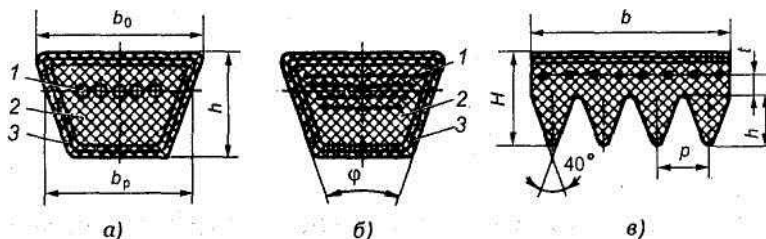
Конструкции клиновых ремней: а — кордшнуровой; б — кордтканевый; в — поликлиновой
